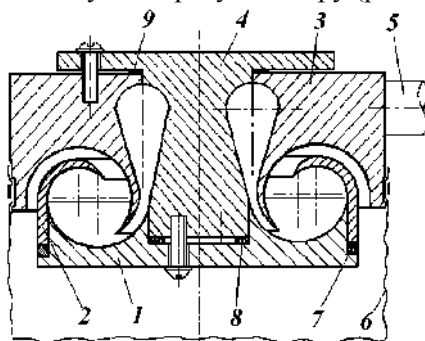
Лабораторный струйно-вихревой аппарат: 1, 2 – формирователи потока; 3 – корпус; 4 – крышка; 5 – патрубок; 6 – рукавный фильтр; 7–9 – прокладки.
